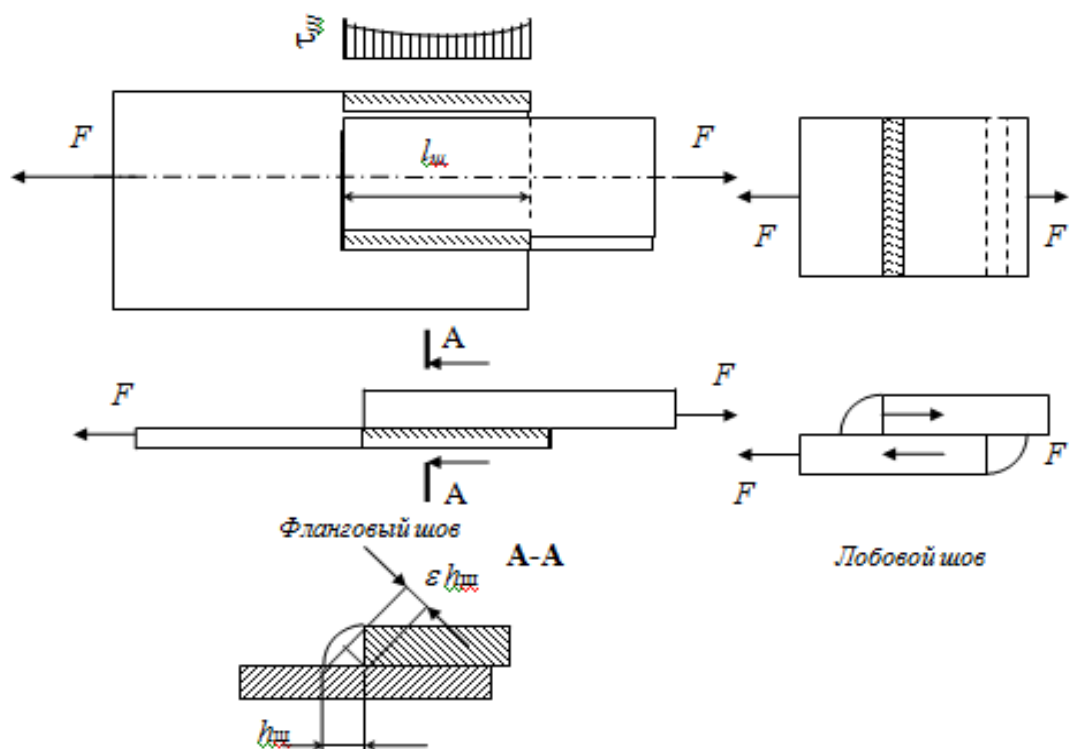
Сварные соединения внахлестку. $l_{ш}$ – длина шва; $h_{ш}$ - толщина шва, принимаемая равной катету вписанного треугольника; ε - коэффициент, зависящий от вида сварки.
